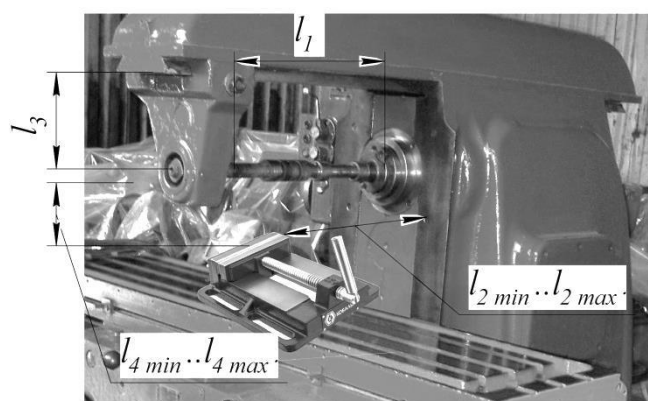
Эскиз рабочей зоны горизонтально-фрезерного станка
